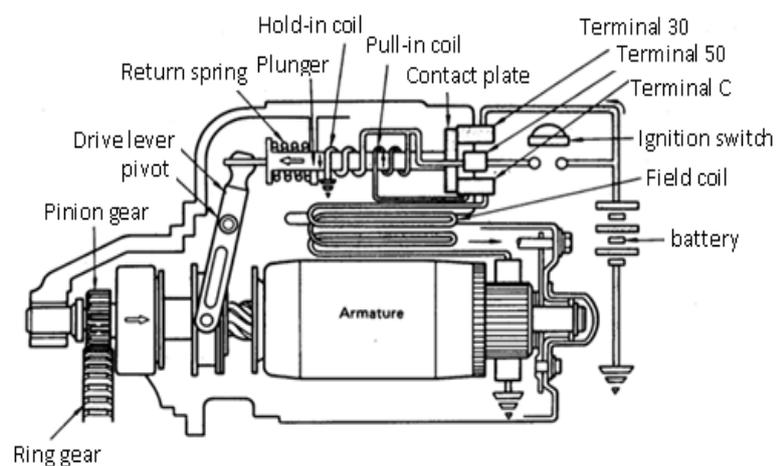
Starter Pada Saat Pinion dan Ring Gear Berkaitan.
